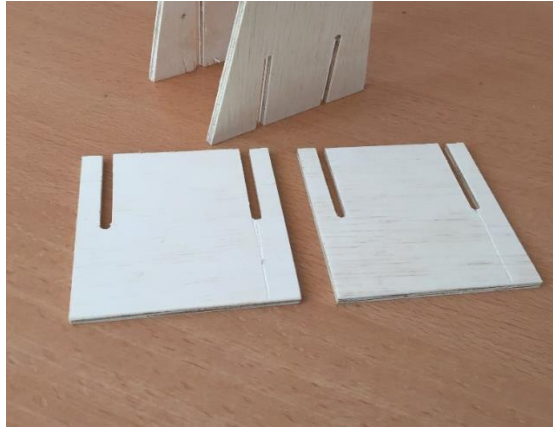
GUIDES POUR LES PIÈCES EN BOIS
